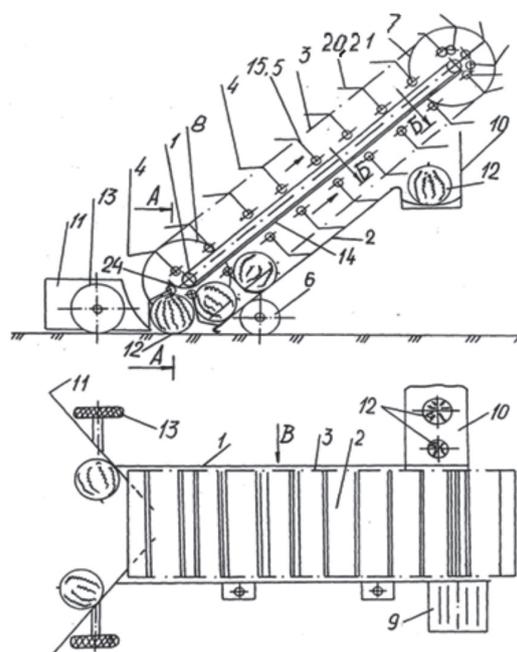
Схема подборщика плодов бахчевых культур: 1 – мобильная рама; 2 – наклонный лоток; 3 – транспортер; 4 – утолщения; 5 – пальцы; 6 – опорные колеса; 7 – ведущий вал; 8 – ведомый вал; 9 – гидромотор; 10 – поперечный транспортер; 11 – валкователь; 12 – плоды; 13 – опорные колеса валкователя; 14 – шина; 15 – лопасти; 24 – концевые участки шины
